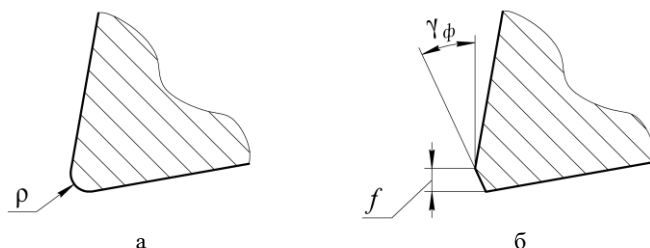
Режущий клин: а – с округлённой режущей кромкой; б – с упрочняющей фаской на режущей кромке
